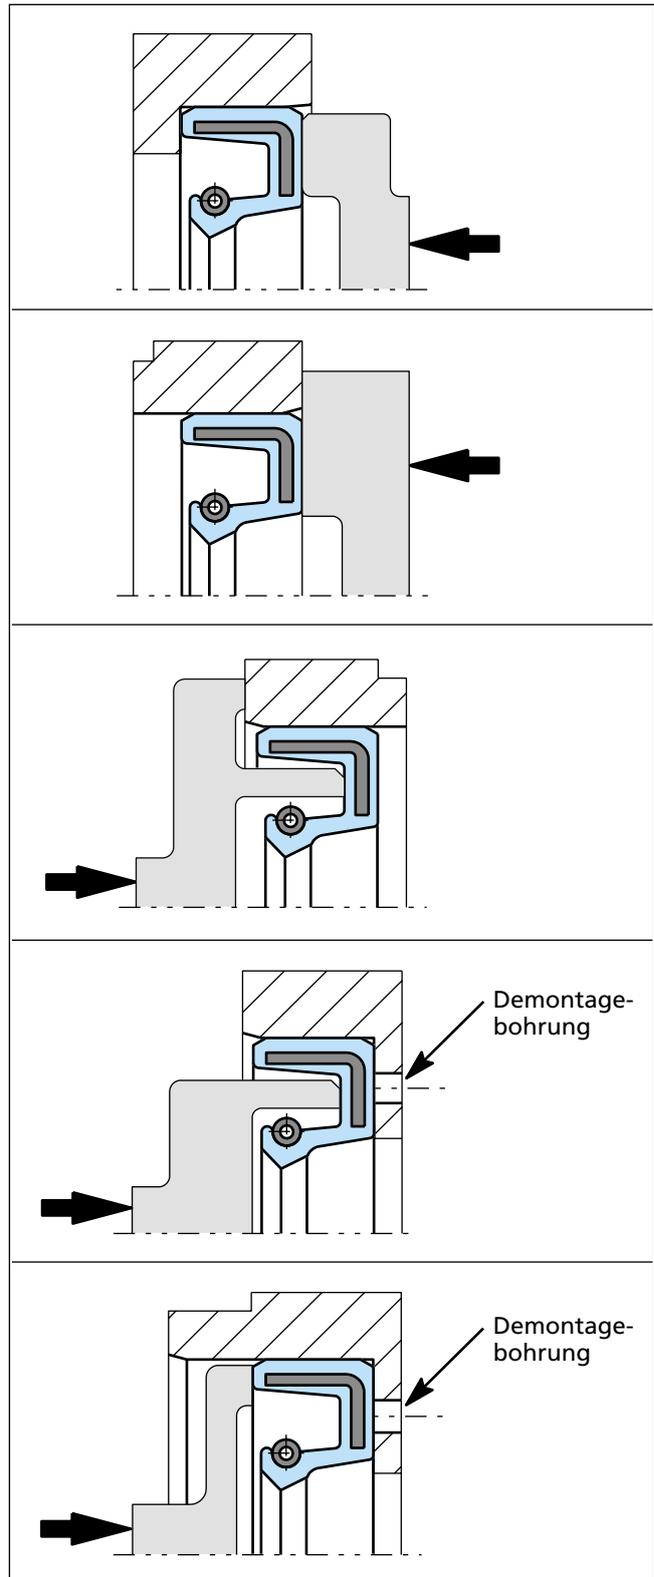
Einbauhilfen bei der Montage von Radial-Wellendichtringen
